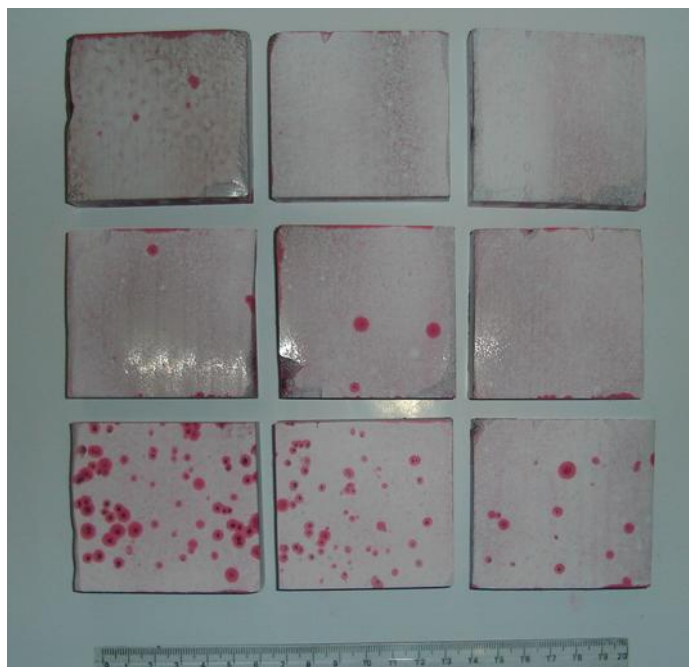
Aplicación del ensayo de líquidos penetrantes en maquinado final
